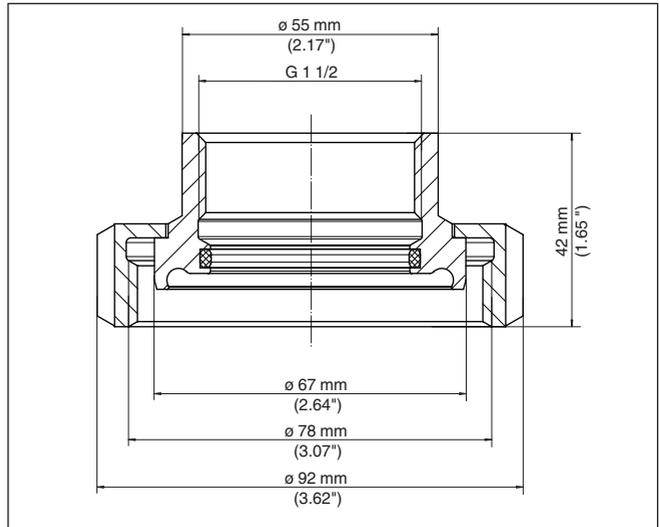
Dimensiones adaptador de rosca G1½ (DIN 3852-X) a racor roscado DN 50 (DIN 11864-1) PN 16
